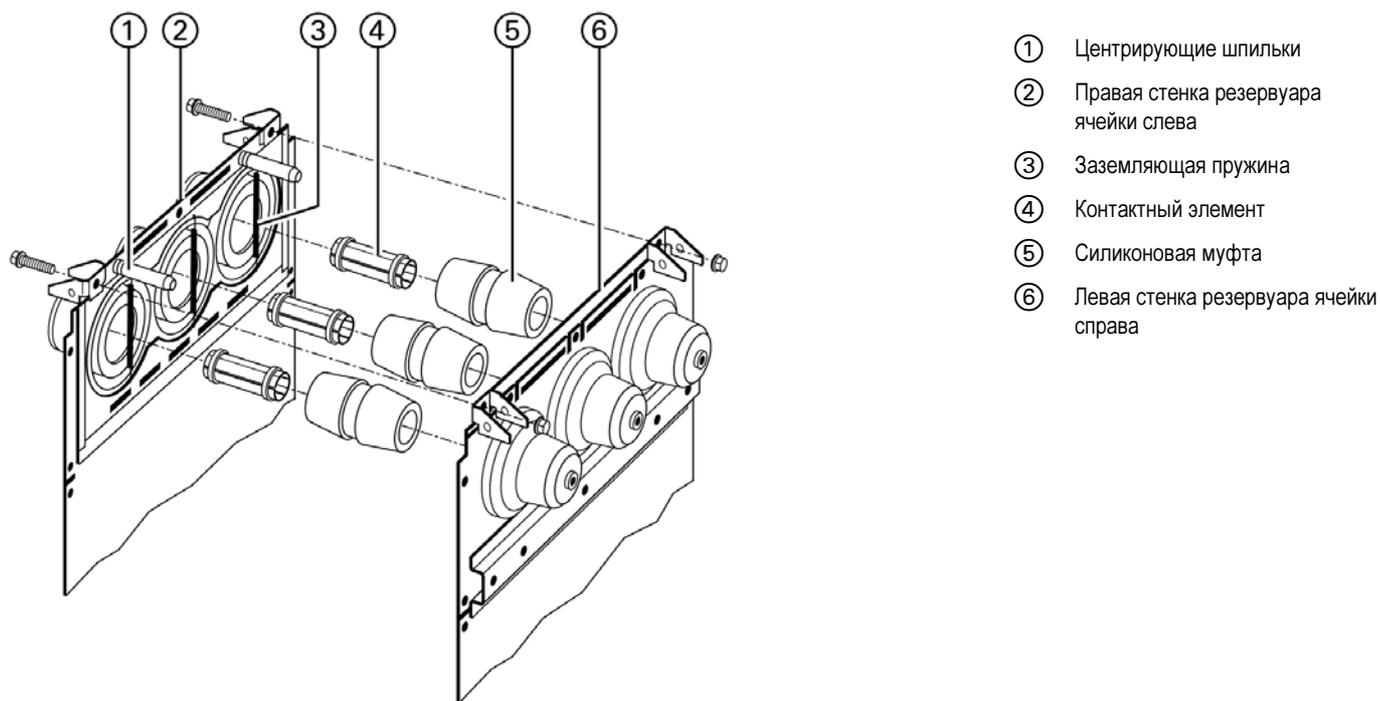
Установка в ряд с помощью соединений сборной шины
